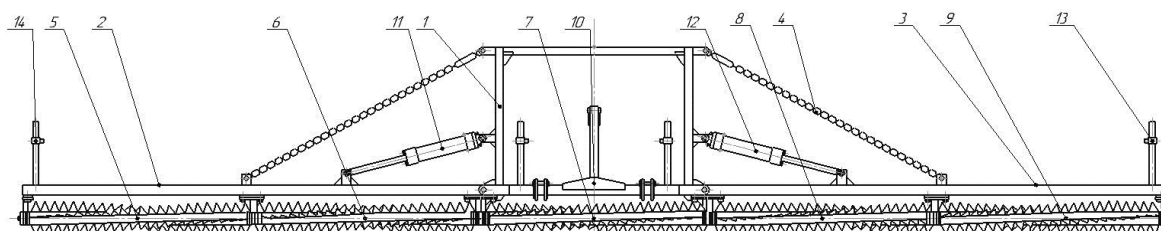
Усовершенствованный фрезер пассивного типа ФПТ-09А (вид сзади).
